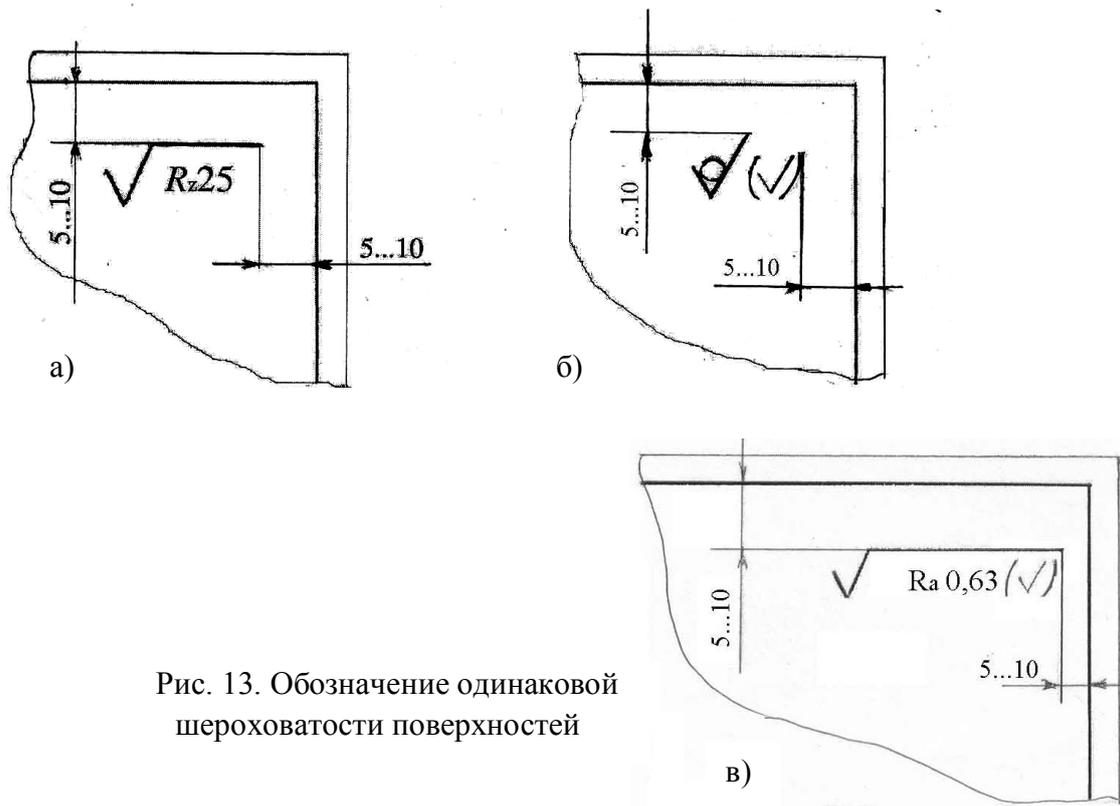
Обозначение одинаковой шероховатости поверхностей
